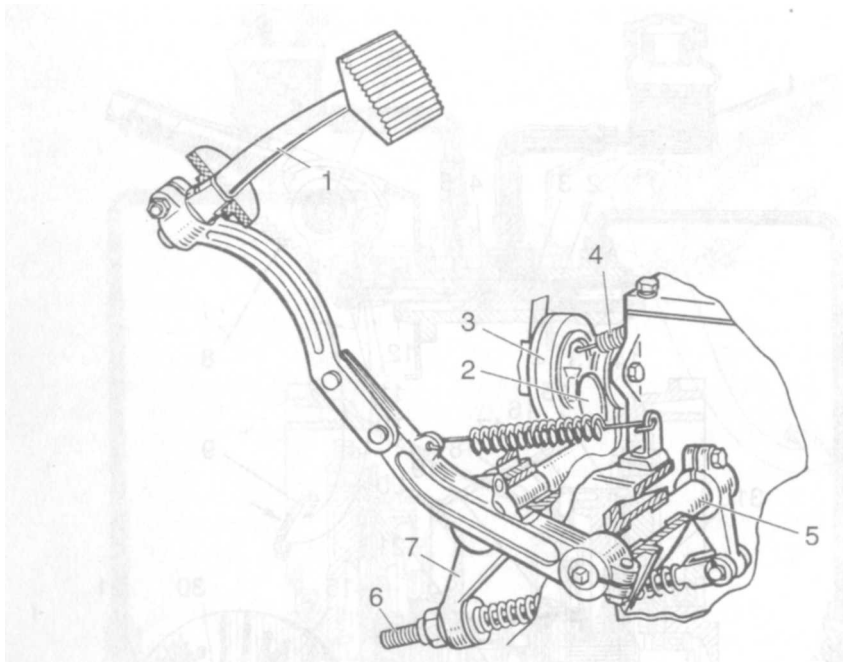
Механічний привод вимикання зчеплення автомобіля ЗІЛ-130: 1 — педаль; 2 — вилка; 3 — витискний підшипник; 4 — поворотна пружина; 5 — вал; 6 — тяга; 7 — важіль
